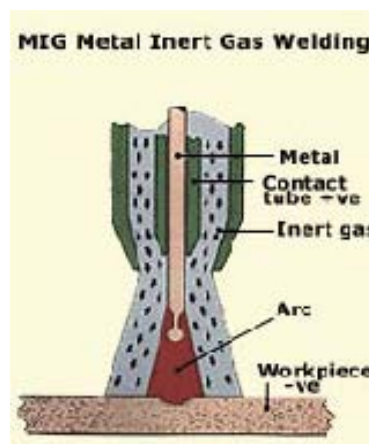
Esquema de elementos del arco de soldadura MIG ⁴⁴
